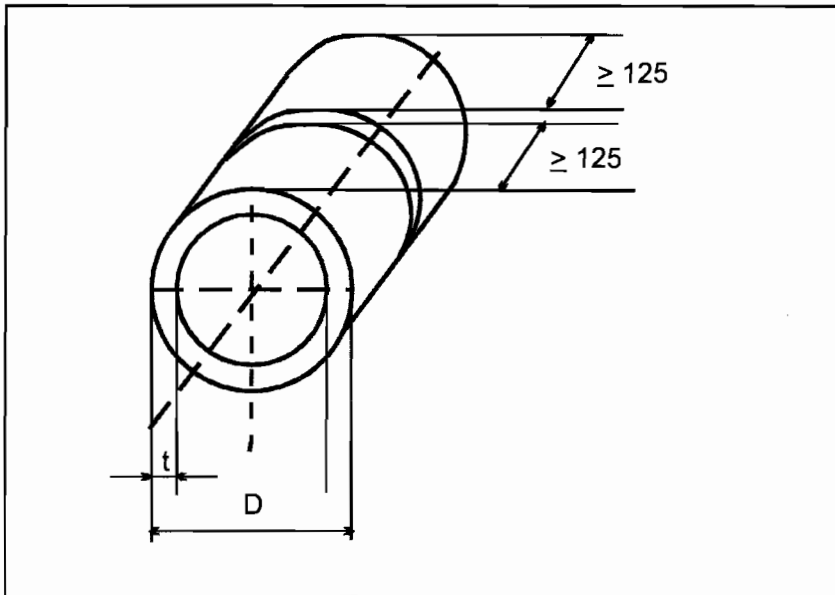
DIMENSIONES DEL CUPÓN DE PRUEBA PARA EL SOLDEO DE TUBOS A TOPE (DIMENSIONES EN MILÍMETROS)
